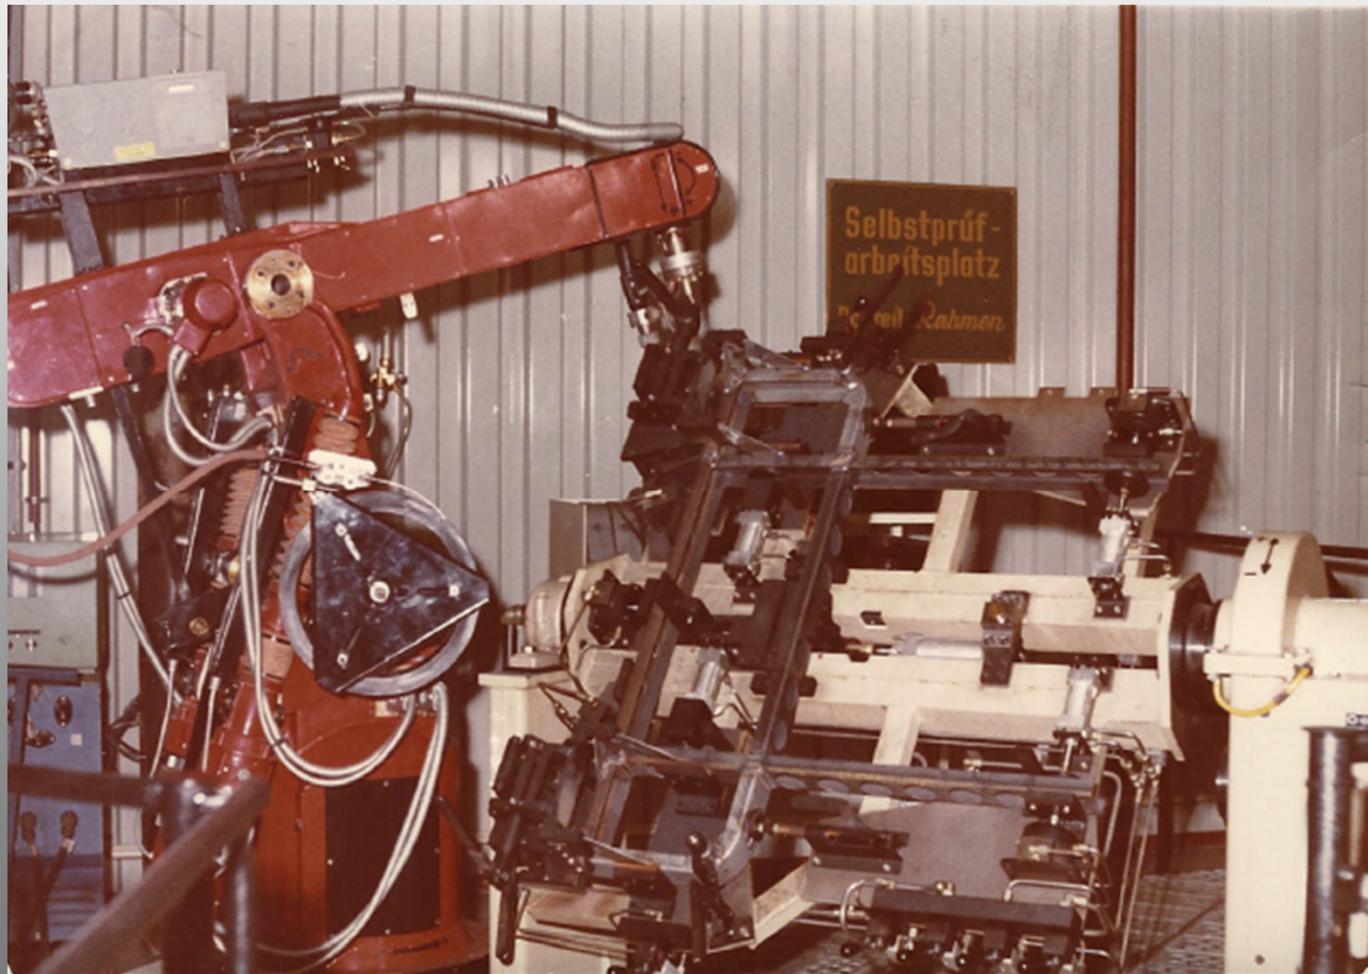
MAG-Schweißroboter ZIM 10 mit Sonderschweißvorrichtung (6. Achse) für Fahrgestell.
